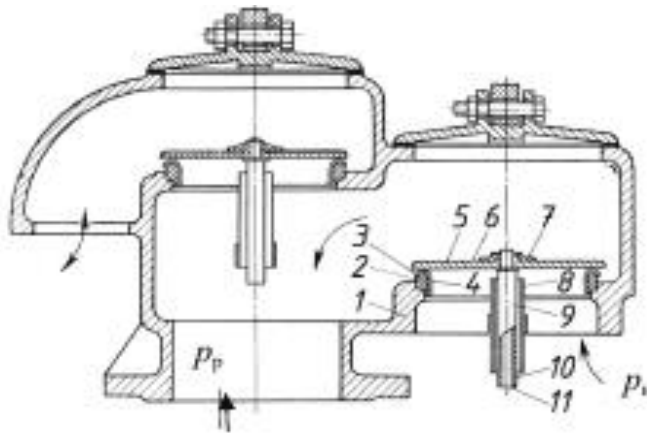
Непримерзаючий механічний дихальний клапан: 1 - корпус;
